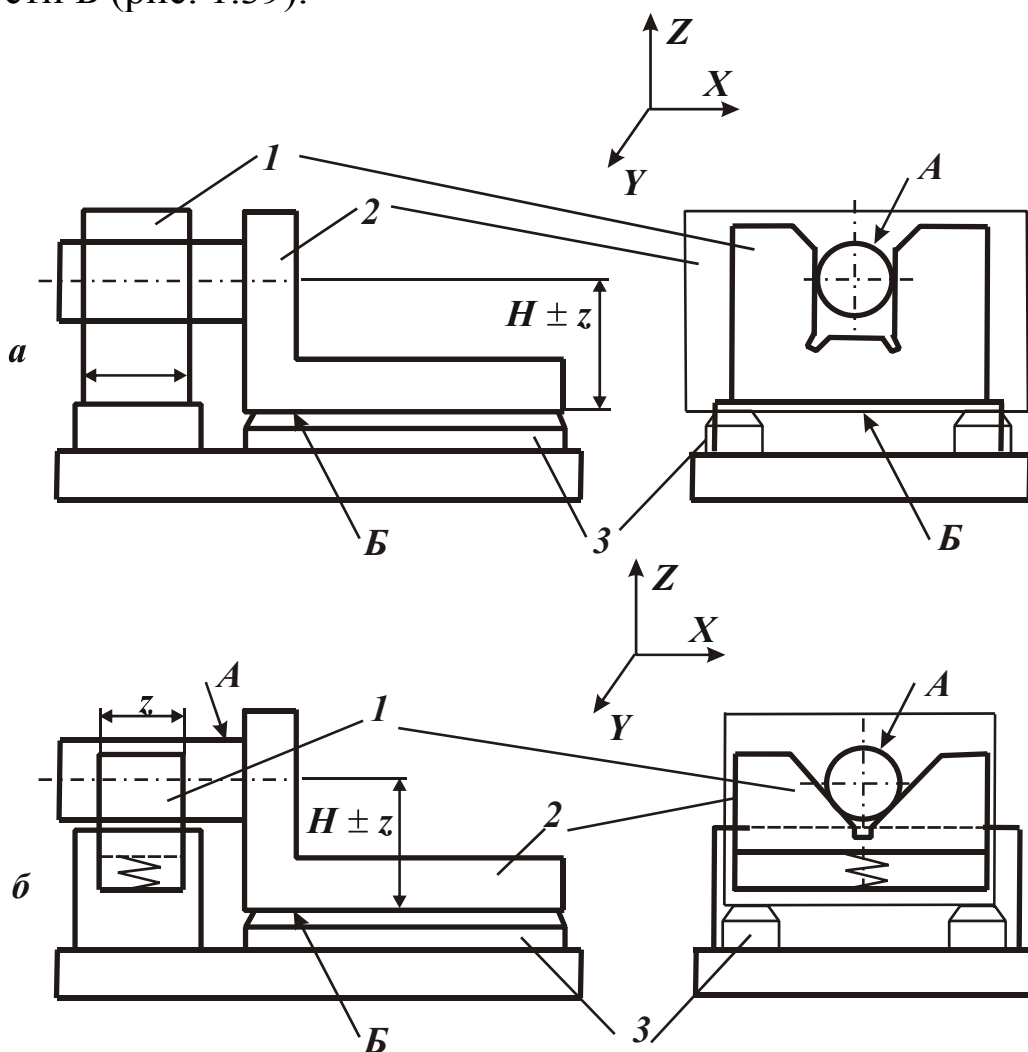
Способы базирования заготовки дополнительной базой в виде наружной цилиндрической поверхности, ось которой параллельна базе, уже получившей базирование.
